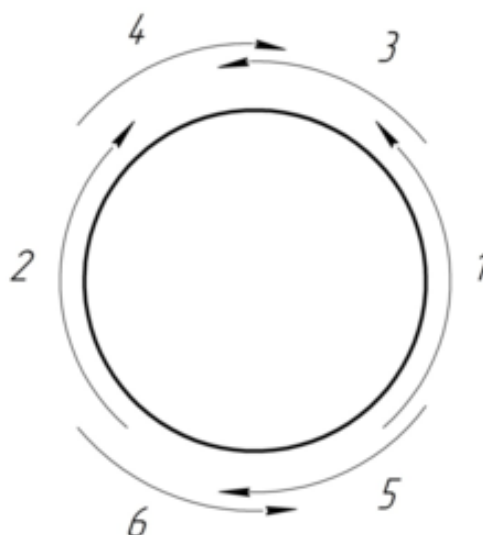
Схема сварки корневого прохода
